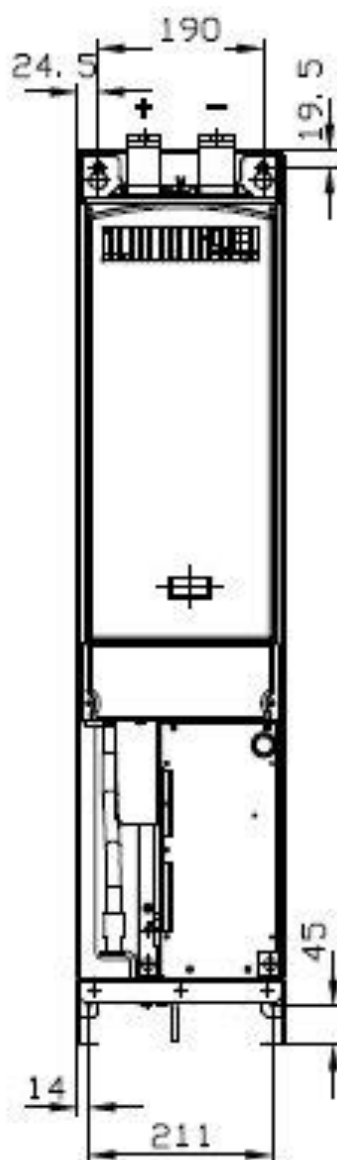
Точки крепления устройства NFE в корпусе F19
